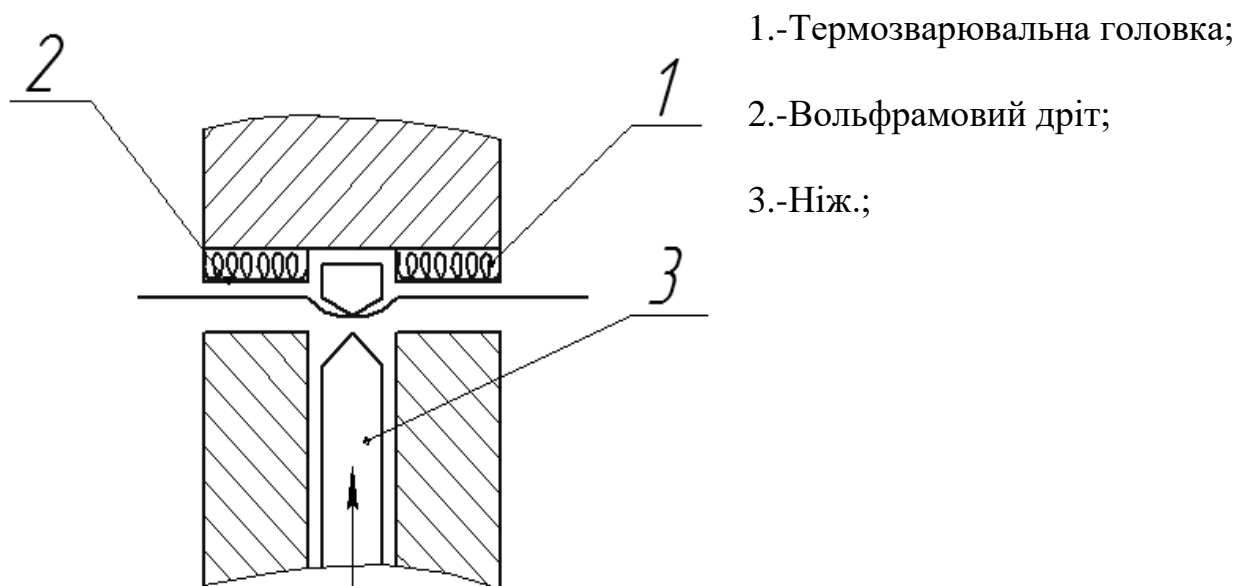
Пристрій для поперечного зварювання плівки.
